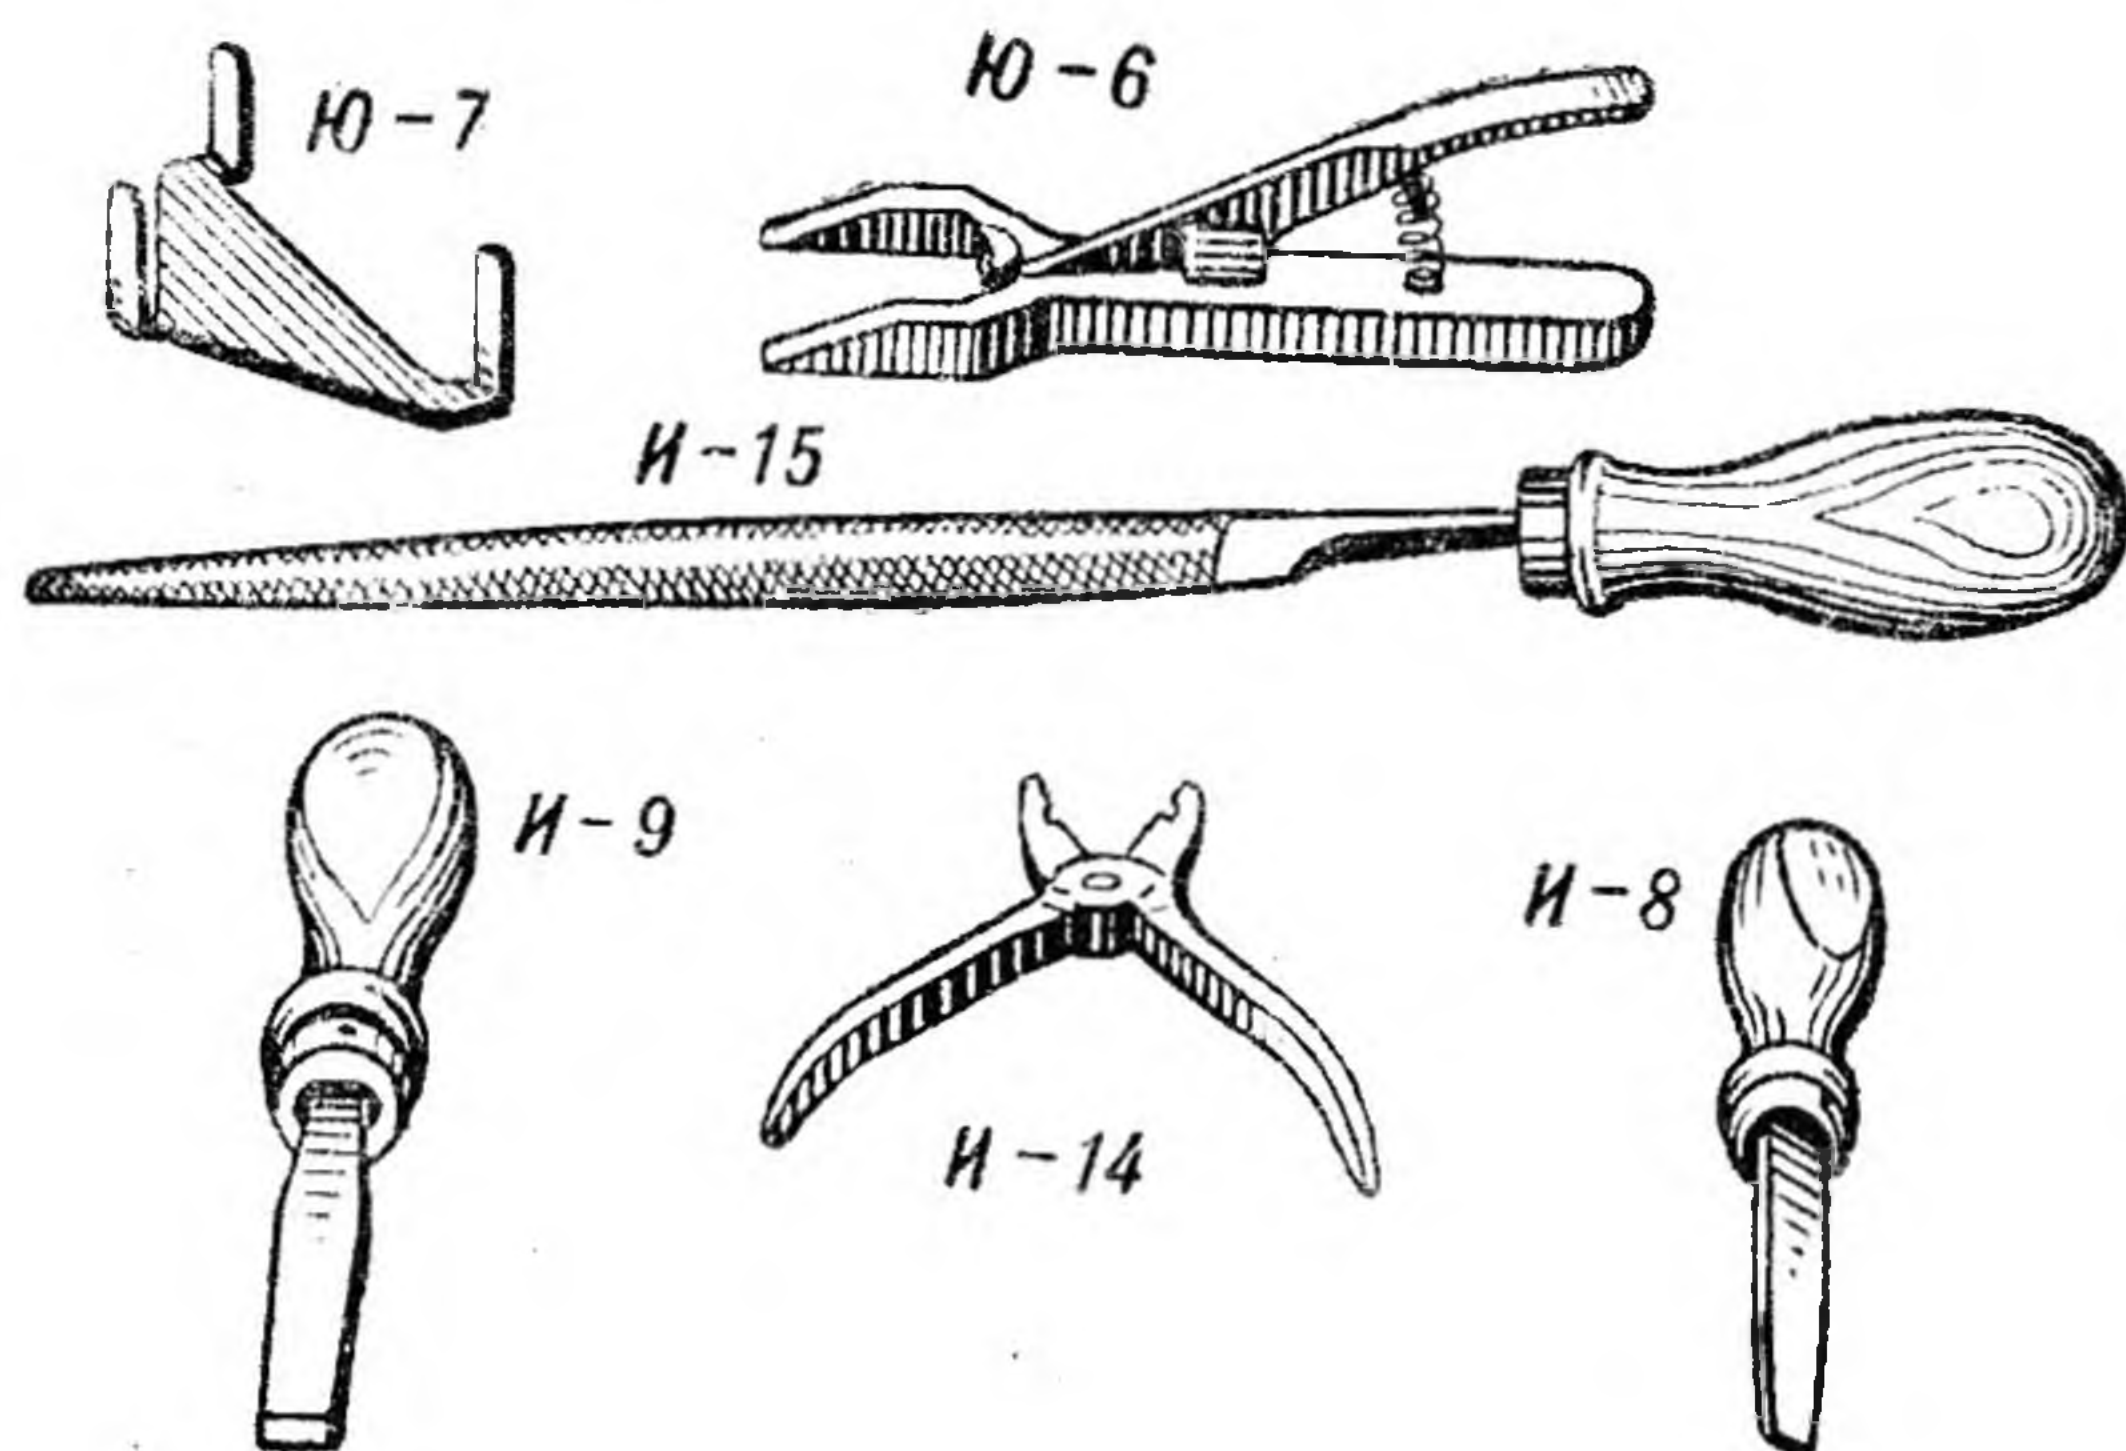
Инструмент для разборки и сборки затвора с полуавтоматикой и ручной экстрактор
